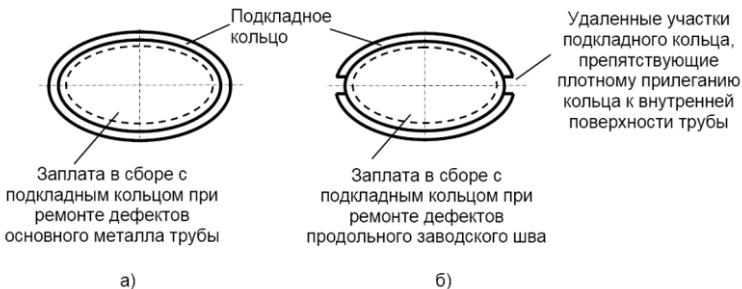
Сборка заплата с подкладным кольцом в овальном отверстии при ремонте дефектов основного металла и сварных швов
